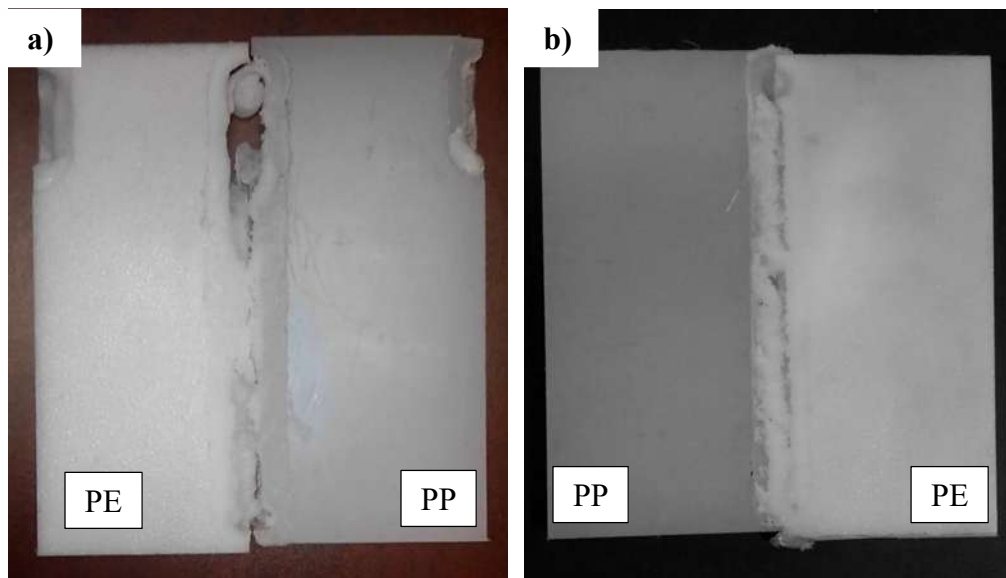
a) Soldadura por fricción-agitación de placas de PP y UHMWPE, parámetros de proceso del ensayo 3, b) parámetros de proceso del ensayo 4.
